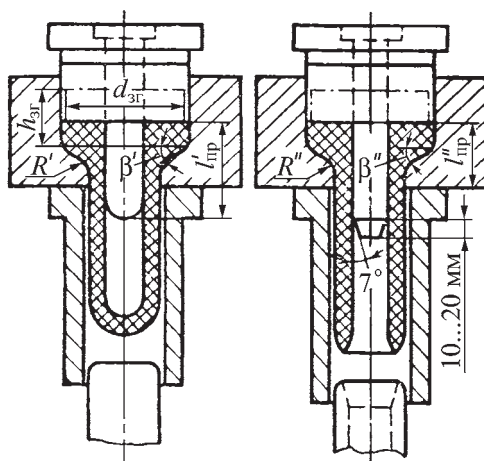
Схема двухпереходной штамповки поковки со сквозным отверстием
